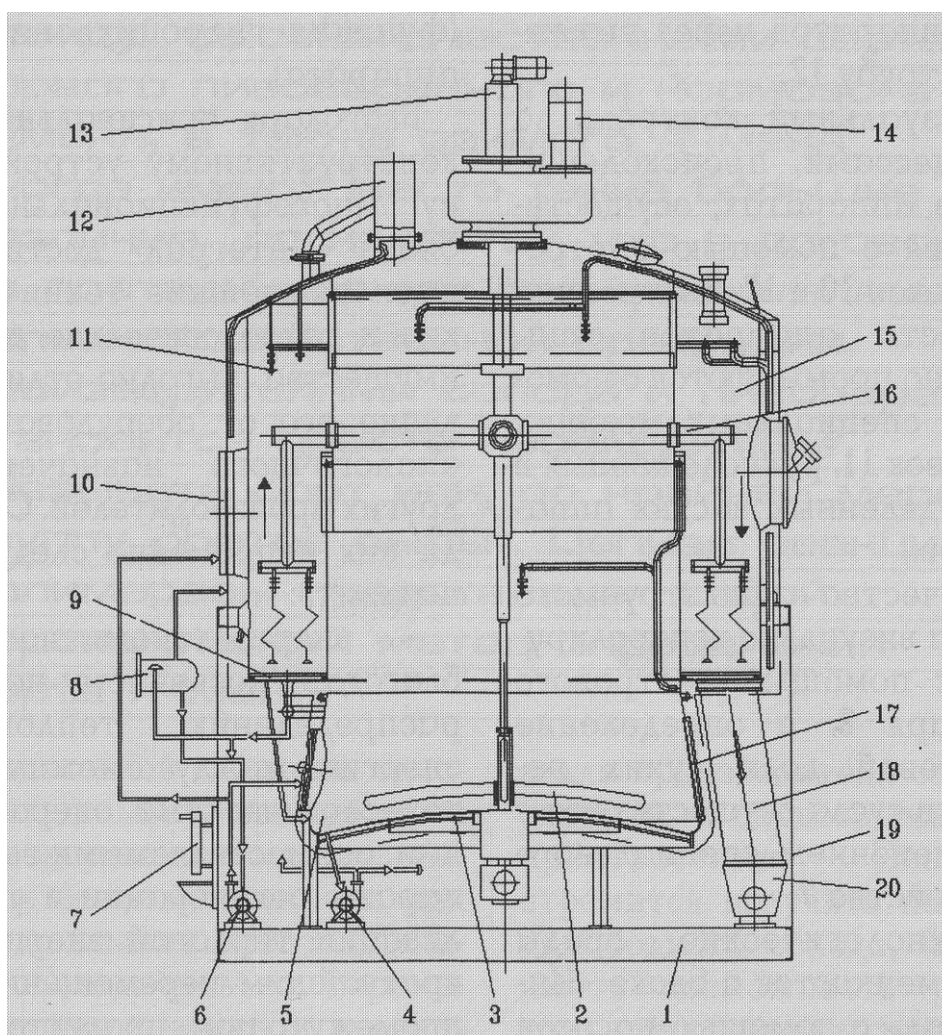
Схема универсального агрегата "Integral" для приготовления сусла
